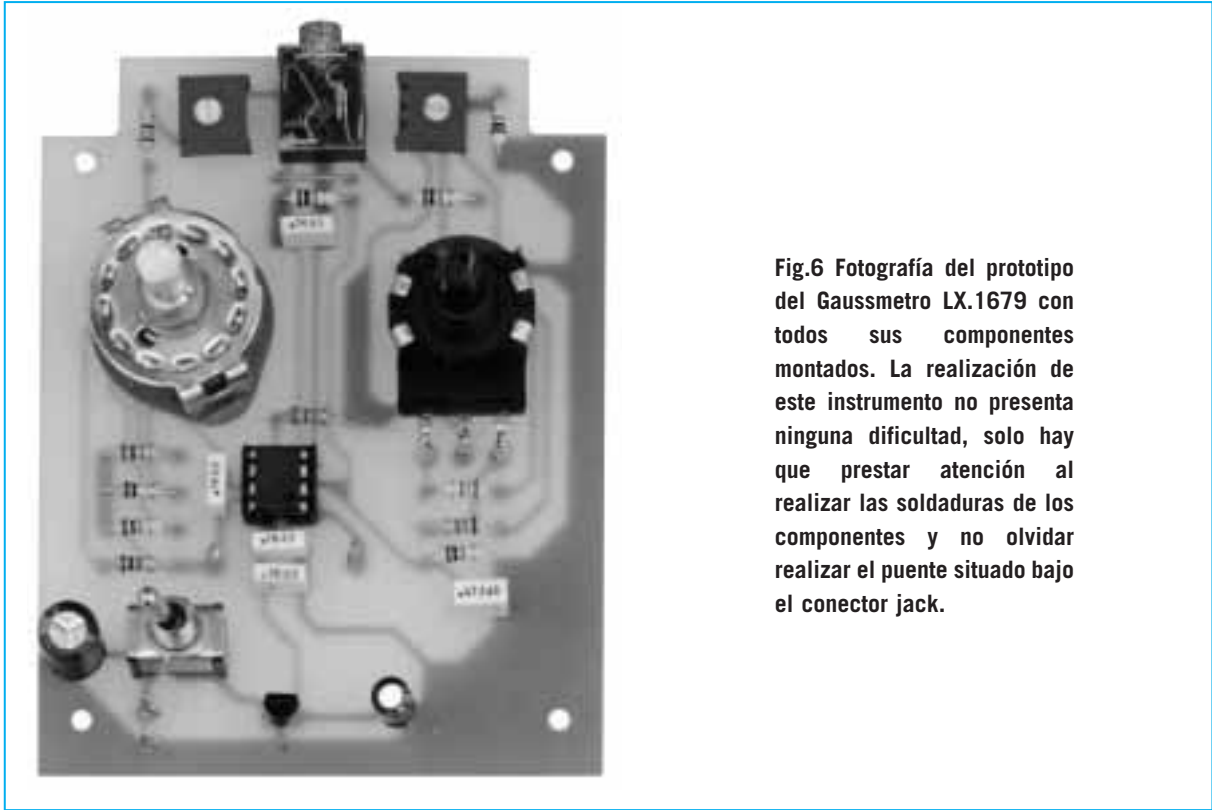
Fotografía del prototipo del Gaussmetro LX.1679 con todos sus componentes montados. La realización de este instrumento no presenta ninguna dificultad, solo hay que prestar atención al realizar las soldaduras de los componentes y no olvidar realizar el puente situado bajo el conector jack.
